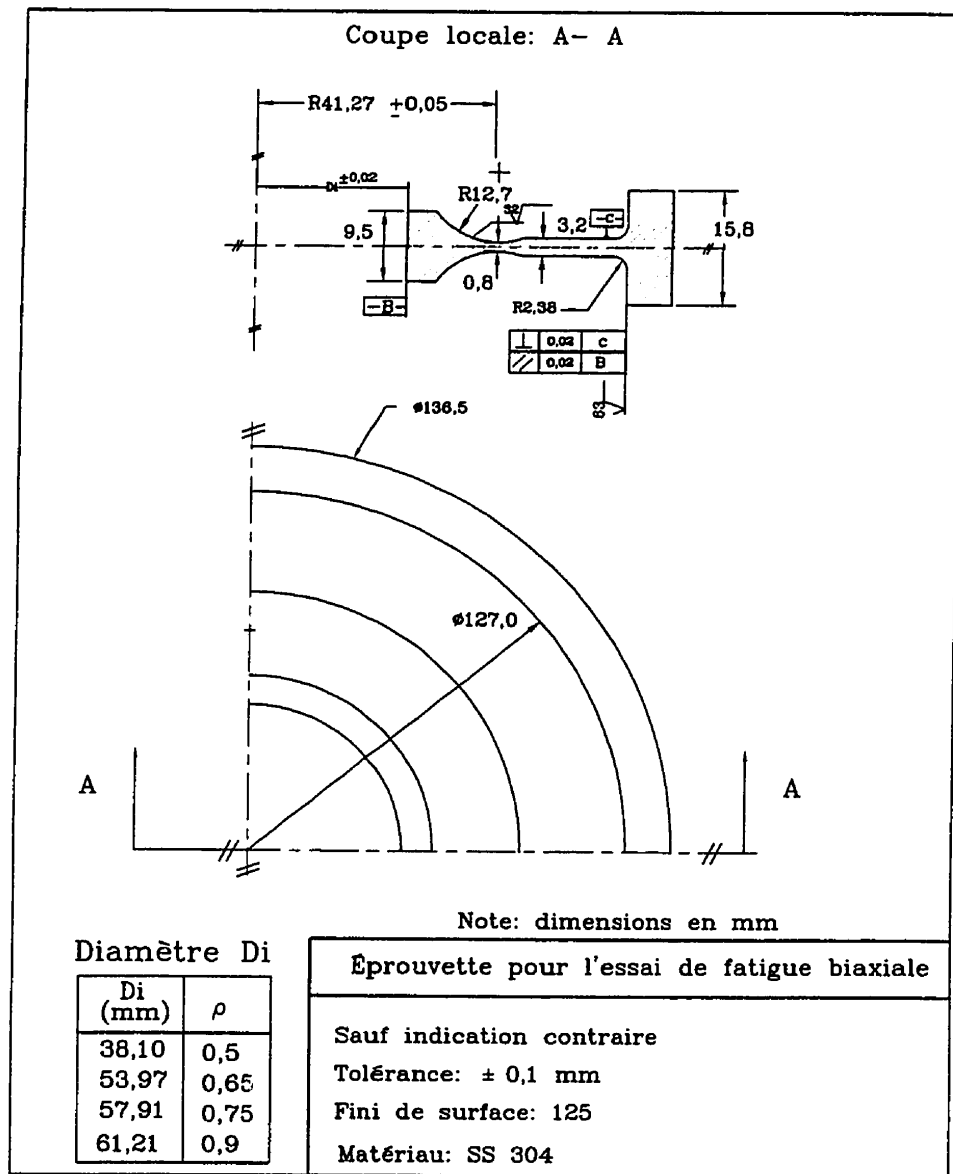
Géométrie et dimensions des éprouvettes d'essai de fatigue biaxiale
